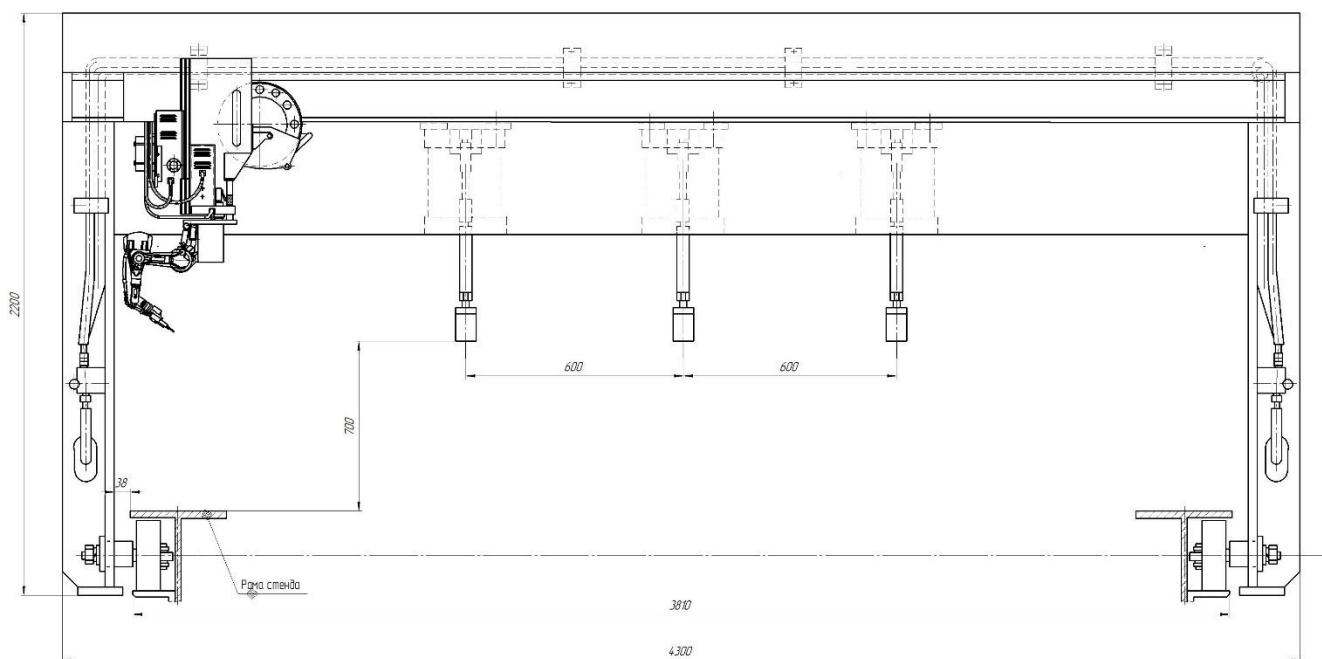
Портальна установка для складання та приварювання стояків до обшивки
